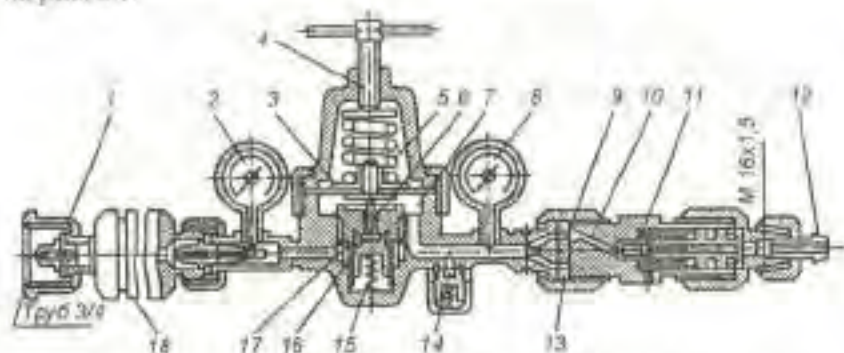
Схема газового редуктора У-30 для вуглекислого газу.
